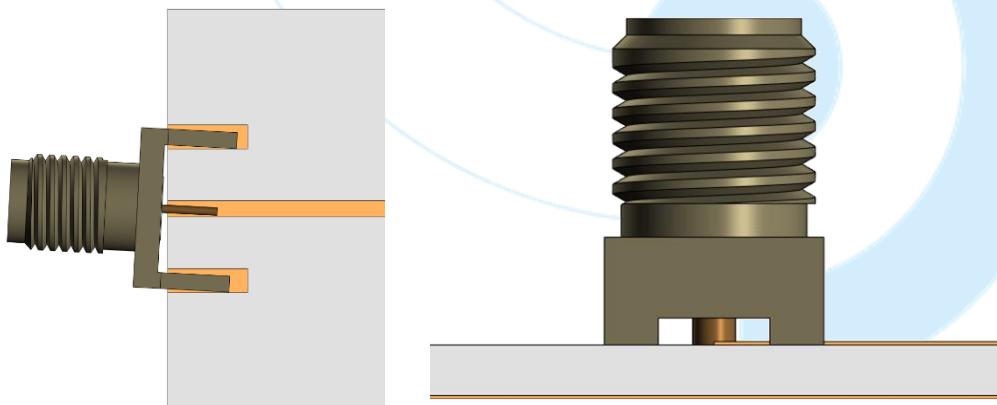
Рекомендуется не допускать щелей между соединителем и платой
